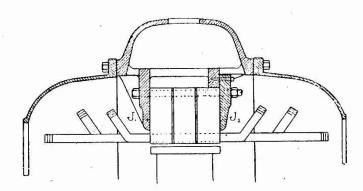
Coupe d'une carcasse avec une joue de serrage indépendante. Enroulement à trois étages de bobines pour haute tension (5000 à 10000 volts).
